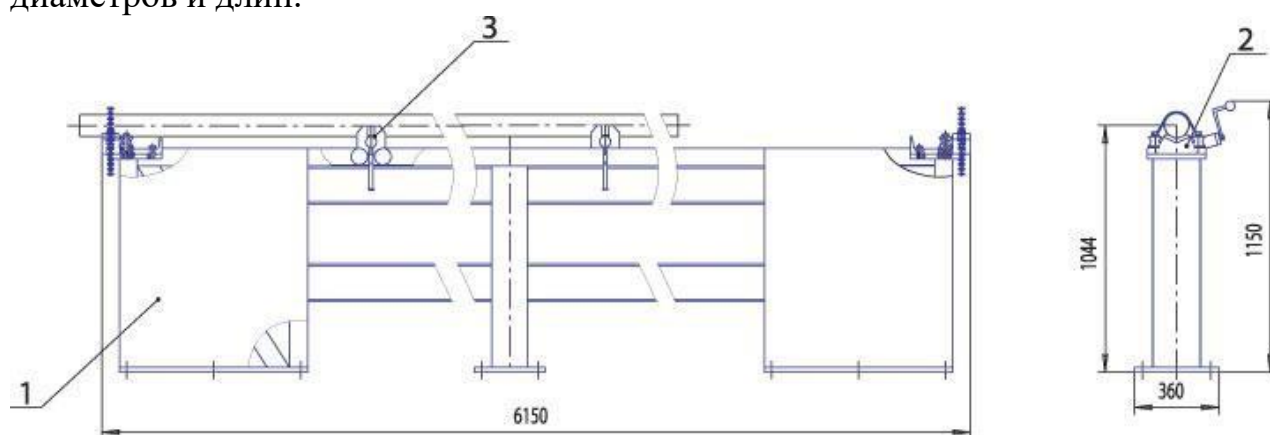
Стенд сборки ЭЦН модели НП03
